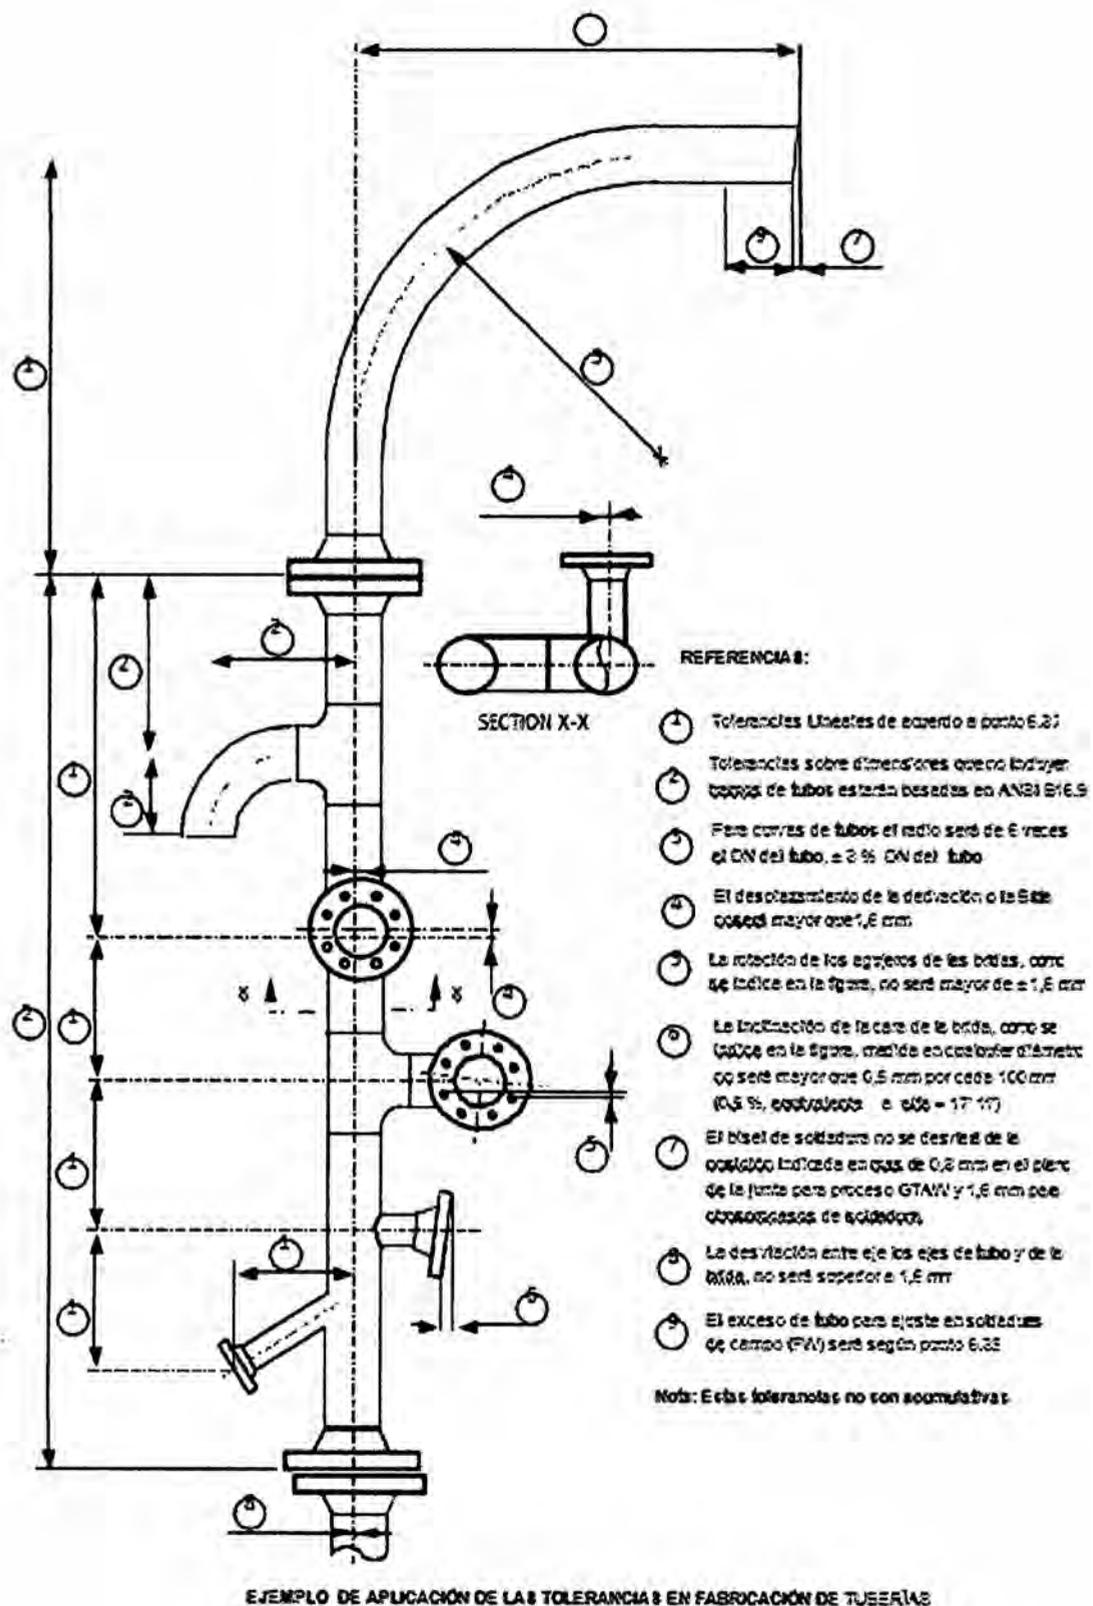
Aplicación de las tolerancias en fabricación de tuberías
